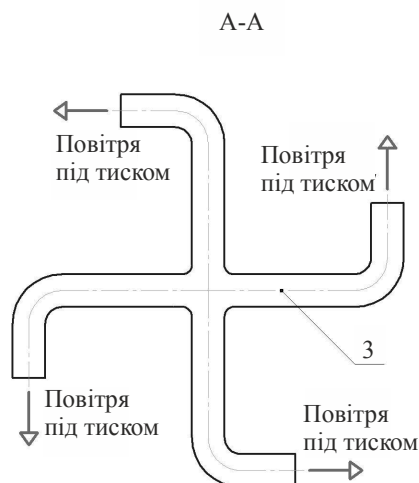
Схема руху повітря через сопла пневматичного перемішувального пристрою
